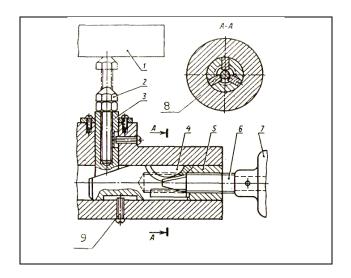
Клиновая дополнительная подводимая опора. 1 – заготовка, 2 – стопорная гайка, 3 – плунжер, 4 – сегментная шпонка, 5 – клиновой плунжер, 6 – винт, 7 – рукоятка, 8 – корпус, 9 – стопорный винт
